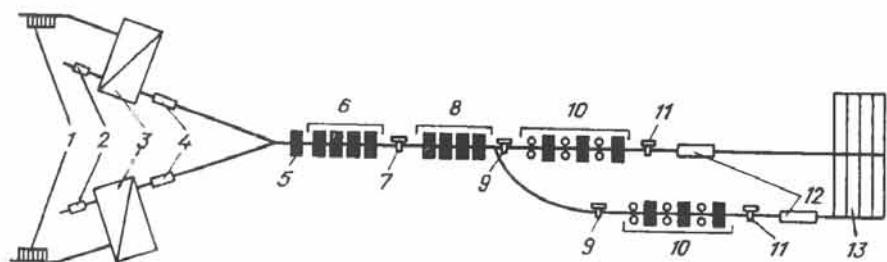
Схема расположения оборудования непрерывного двухниточного мелкосортного стана 250:
